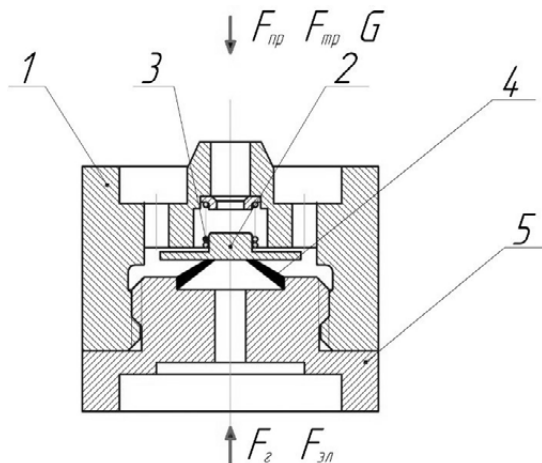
Расчетная схема самодействующего клапана с эластомерным конструктивным элементом: 1 – корпус клапана, совмещенный с ограничителем подъема; 2 – запорный орган (пластина); 3 – пружина; 4 – эластомерный элемент; 5 – седло клапана; F_2 – суммарная сила, действующая на пластину со стороны газа; $F_{эл}$ – сила упругости эластомерного элемента; $F_{пр}$ – сила упругости пружины; $F_{тр}$ – сила трения газа; G – вес запорного органа
